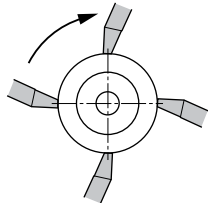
Проверка осевой выверки при помощи штангенциркуля – контроль по периметру
